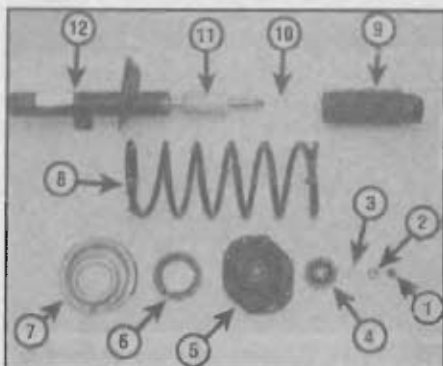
Элементы амортизаторной стойки передней подвески: 1 — защитная крышка; 2 — гайки крепления штока амортизатора; 3 — шайба; 4 — упорная шайба с буртиком; 5 — опорная пластина; 6 — подшипник; 7 — верхнее гнездо пружины; 8 — цилиндрическая пружина; 9 — защитный чехол; 10 — плоская шайба; 11 — резиновый упор; 12 — корпус стойки
